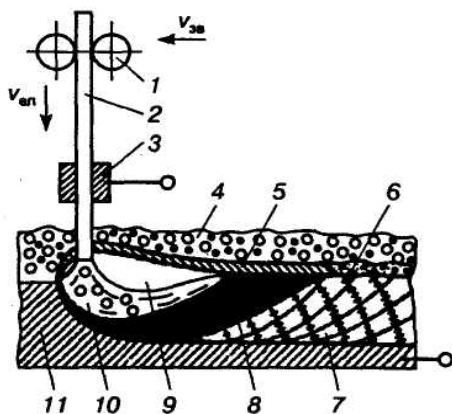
Схема автоматичного дугового зварювання під флюсом
